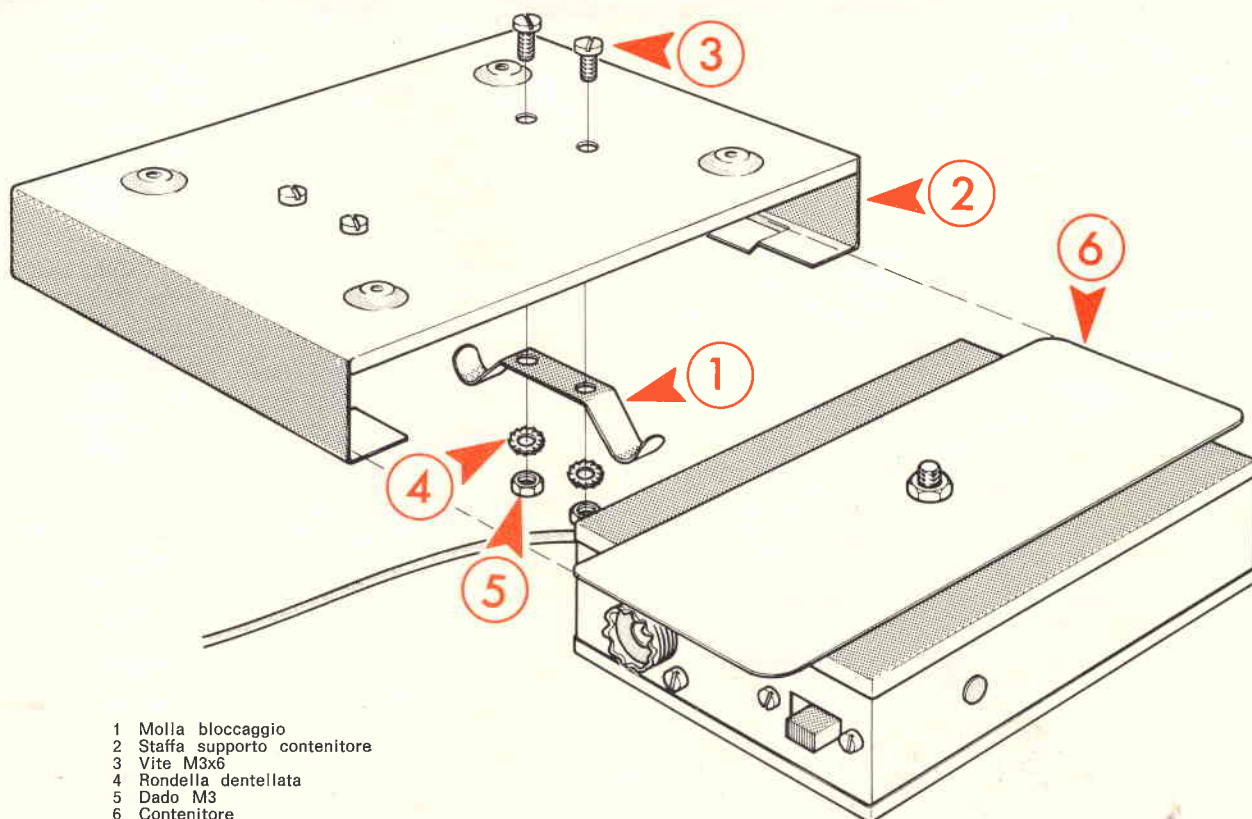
Montaggio del supporto per l'attacco in auto.
